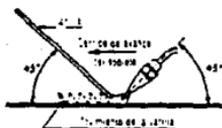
Esquema de soldadura oxiacetilénica horizontal.
